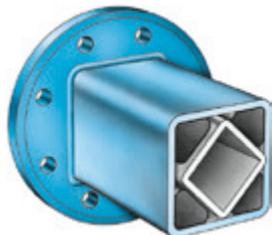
Aussenrohr mit aufgeschweisstem Flansch
